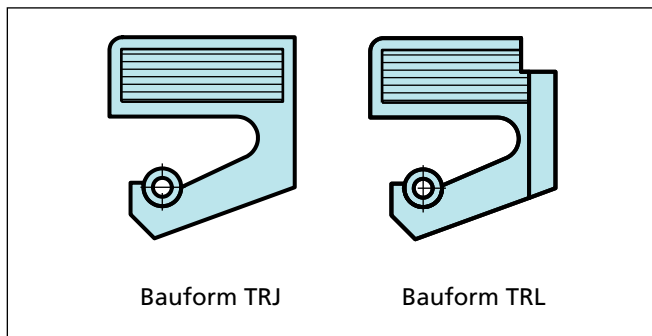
Gewebeverstärkte Ausführungen für große Durchmesser
